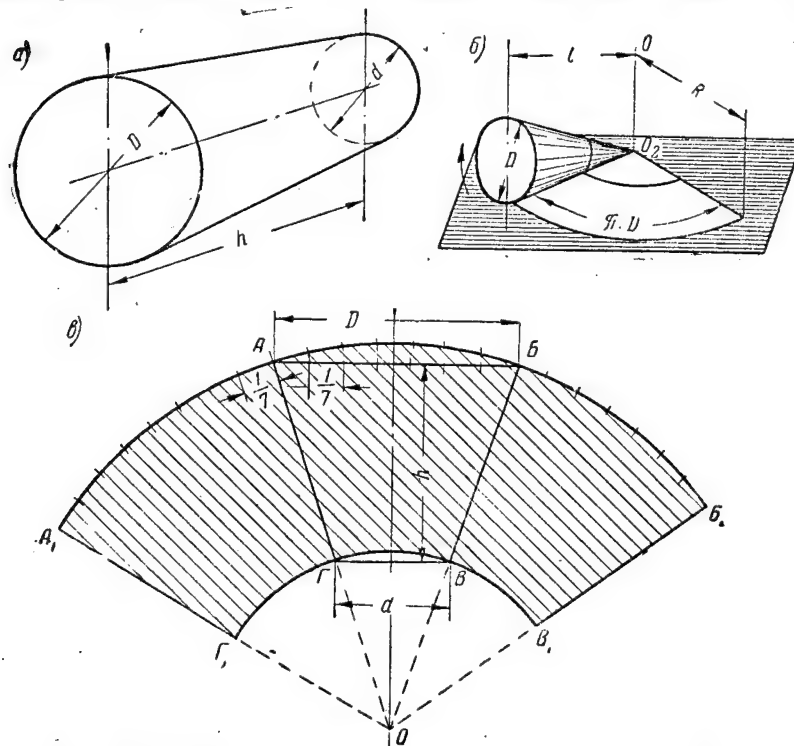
Развертка цилиндрического перехода: *а* — конус; *б* — развертка конуса; *в* — построение цилиндрического перехода.
